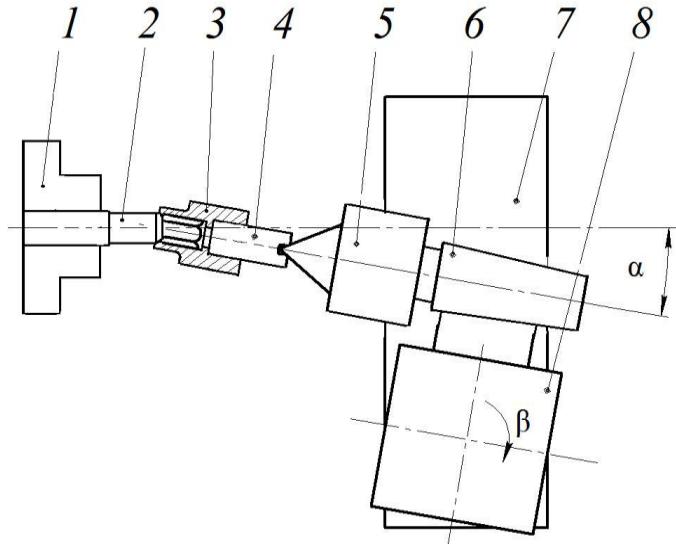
Виготовлення профільних отворів на верстатах токарної групи шляхом ротаційного формоутворення із само встановленням матриці
